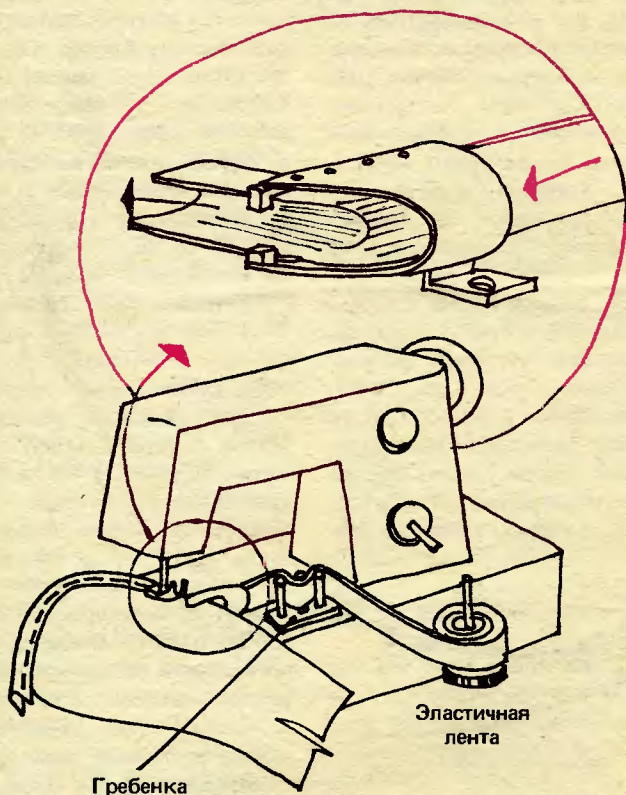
Приспособление для обработки края клапана широкой эластичной тесьмой
